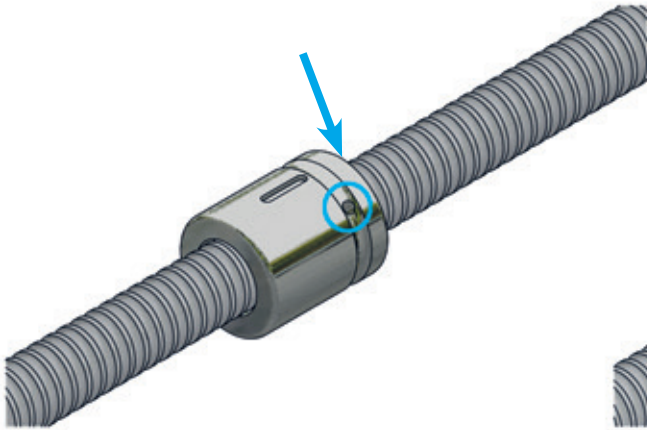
Zylindrische Mutter mit Schmierbohrung
